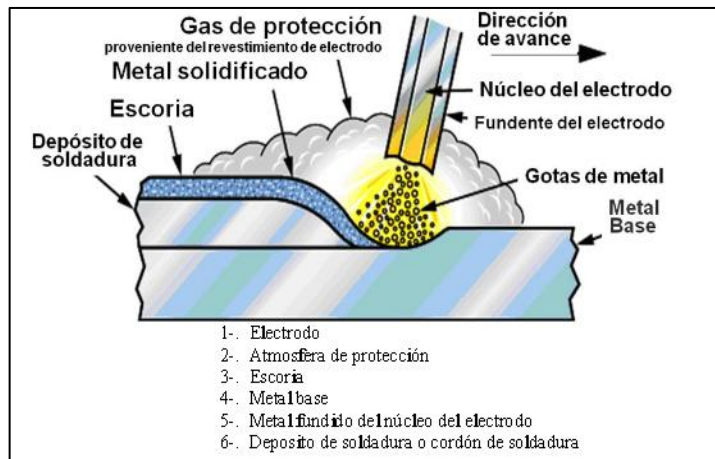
1: Diagrama esquemático del proceso de soldadura SMAW
